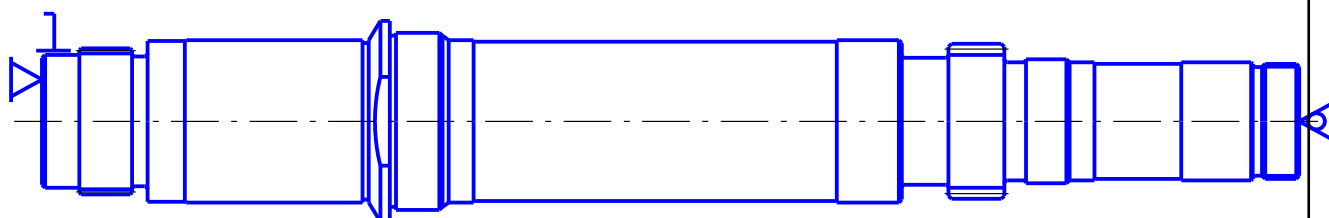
Установка вала в нерухомому передньому центрі з повідковим патроном і обертовому заднім центрі (операції: Токарна, Шліфувальна, Шліцефрезерна, Шліцешліфувальна)
